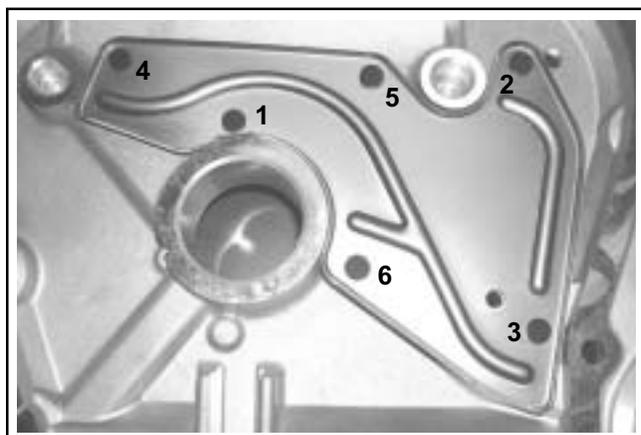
Sequenza di serraggio del carter dei condotti.
